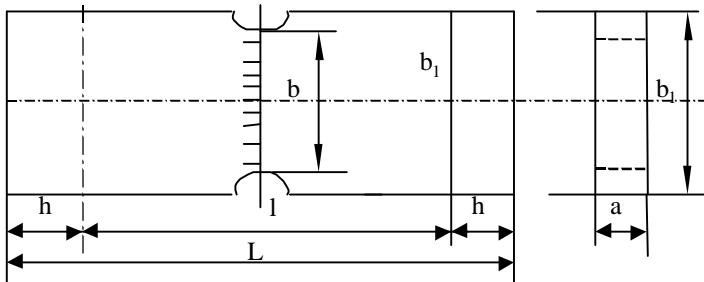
Образец для определения прочности металла сварного шва ( $b_1$ ,  $h$  – размеры захватной части,  $l$  – длина рабочей части)
